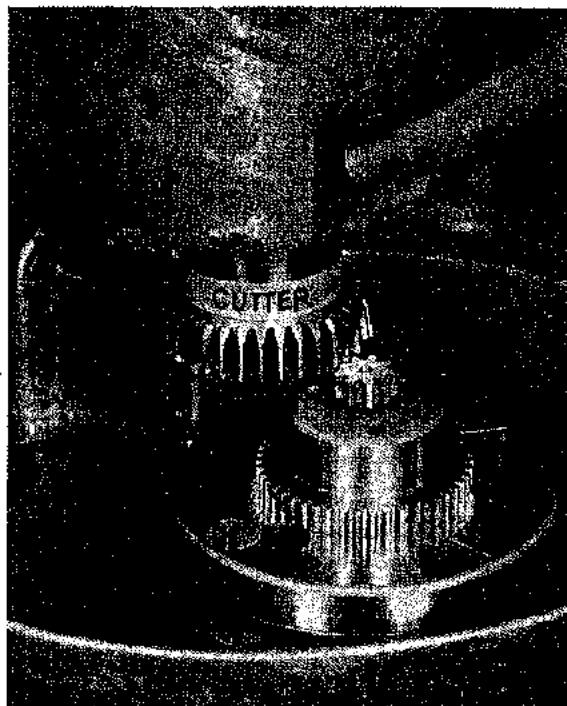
El piñón mortajador se parece a una rueda dentada (Fellows Gear Shaper Co.)
